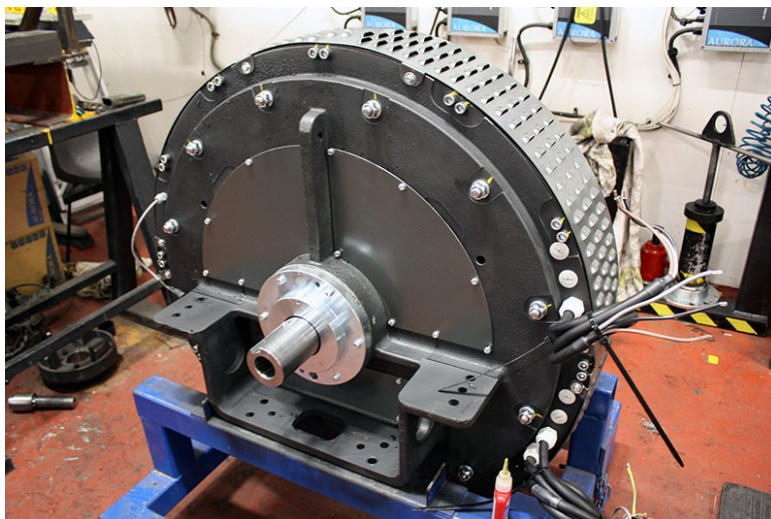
Generátor vyrobený firmou EXMONT[5]
